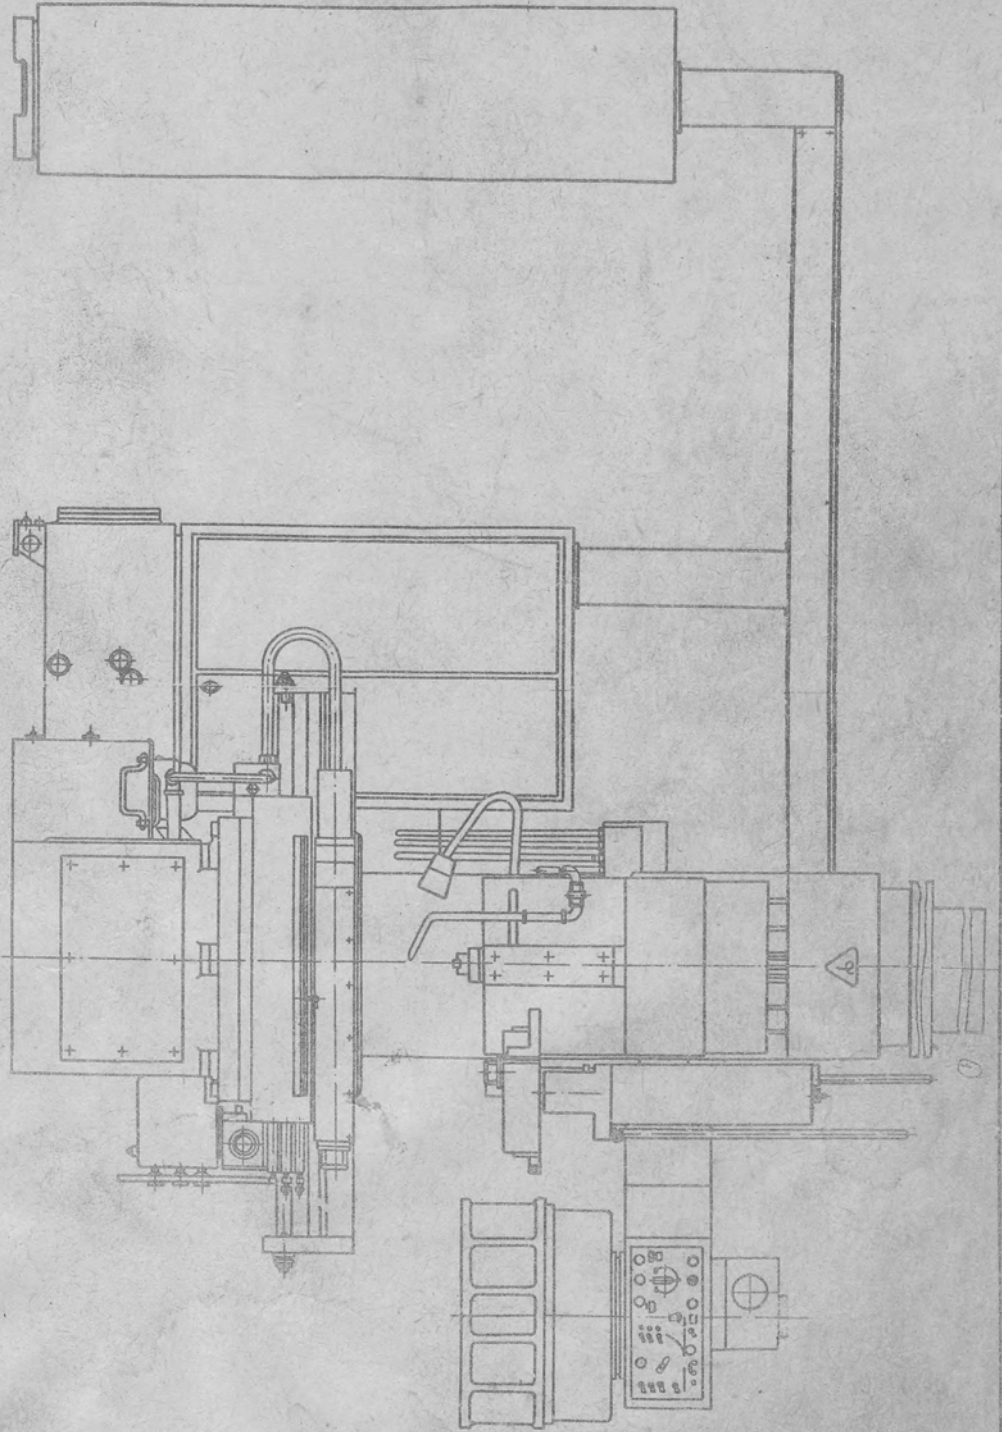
Полуавтомат вертикально-фрезерный с крестовым столом, ЧПУ и автоматической сменой инструмента.
